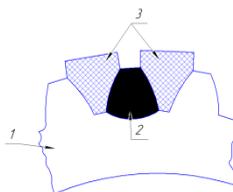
Метод наплавки зубьев сваркой:
